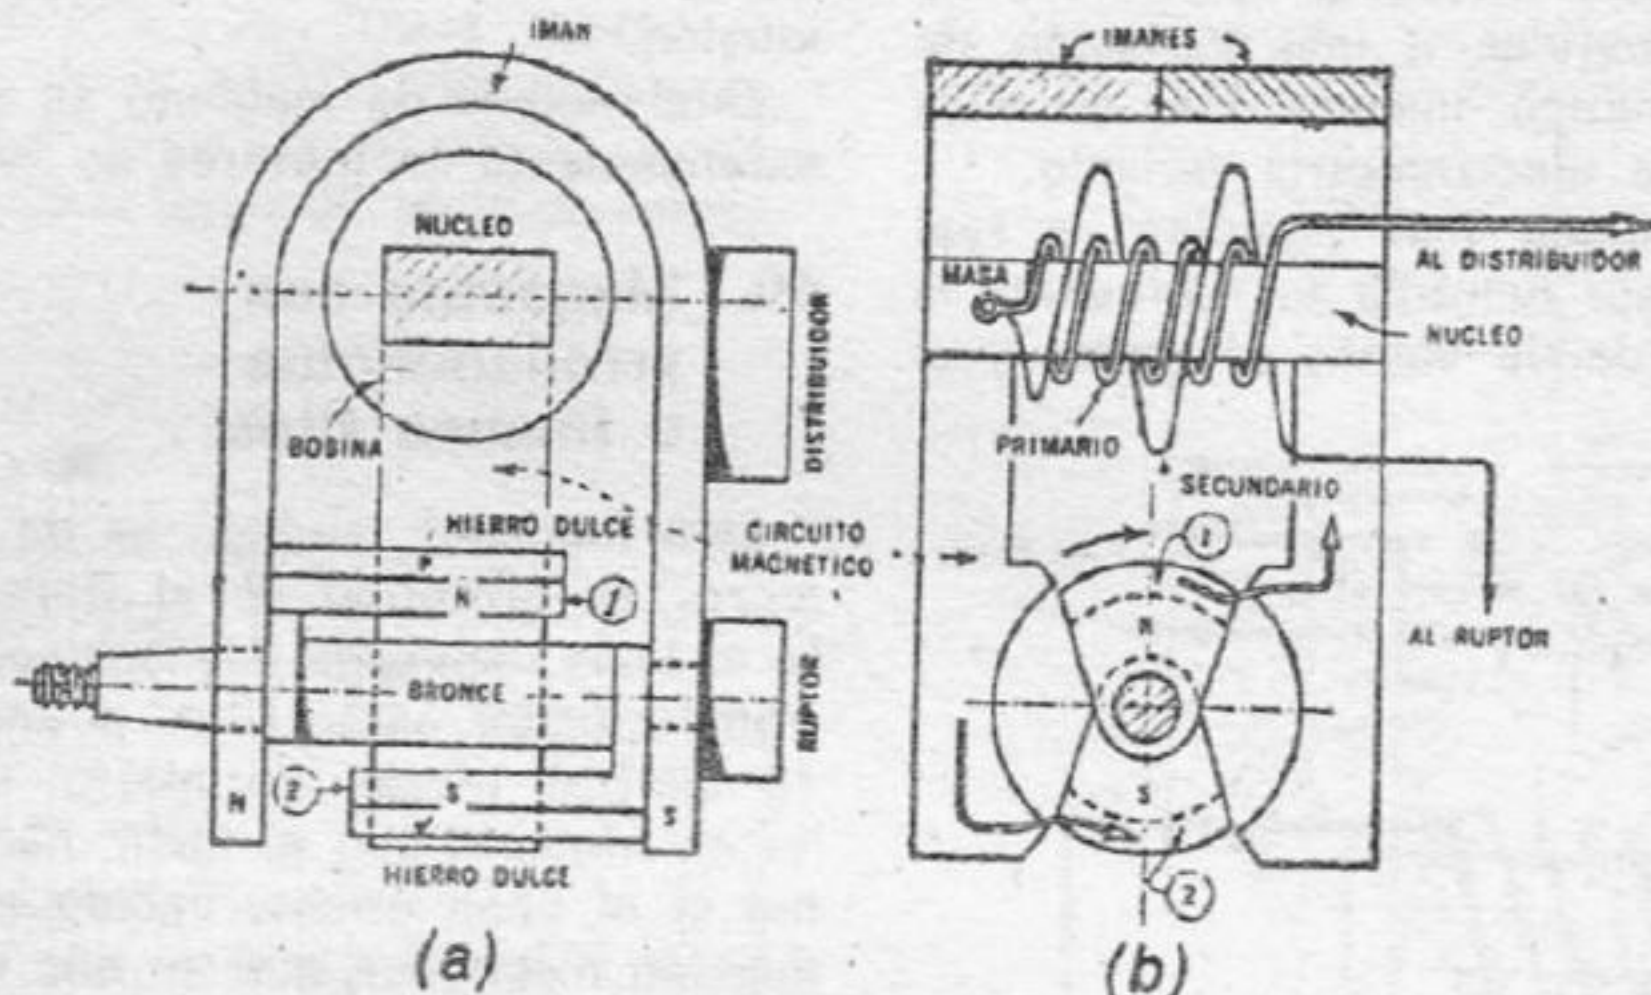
Principios fundamental de la magneto con bobinas e imán fijo.
